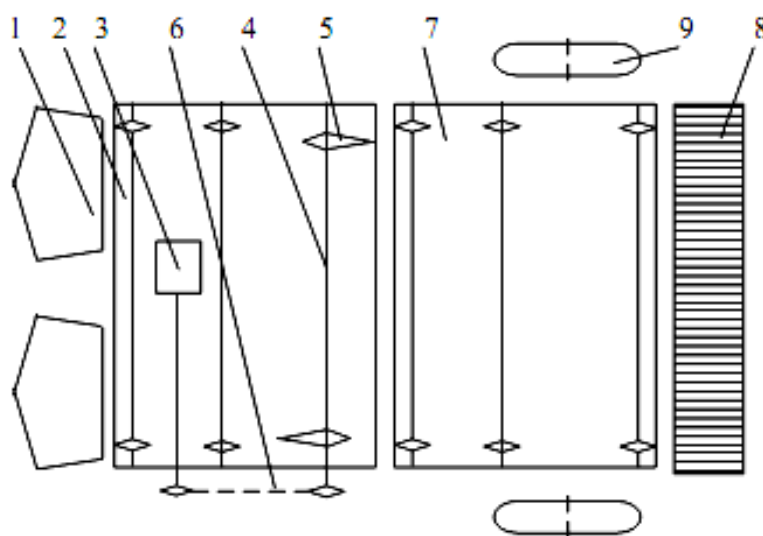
Модернізований картоплекопач: 1 – леміші; 2 – перше елеваторне полотно; 3 – редуктор; 4 – привідний вал; 5 – ексцентрикові привідні зірочки; 6 – ланцюгова передача; 7 – друге елеваторне полотно; 8 – скатна решітка; 9 – ходове колесо
